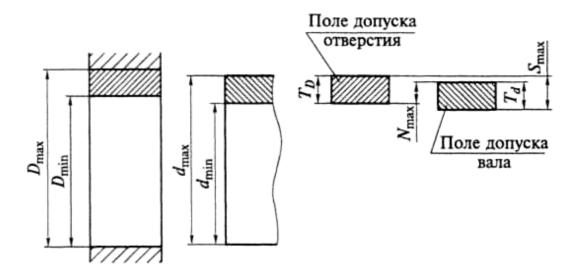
Схемы расположения полей допусков при переходных посадках
